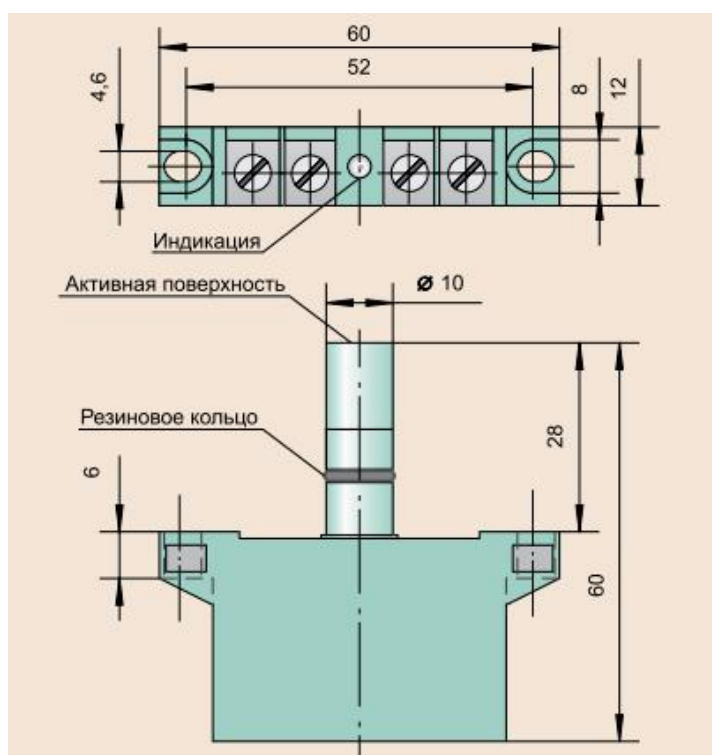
Габаритный чертеж датчика ВБИ-Б10-60К-1113-3
